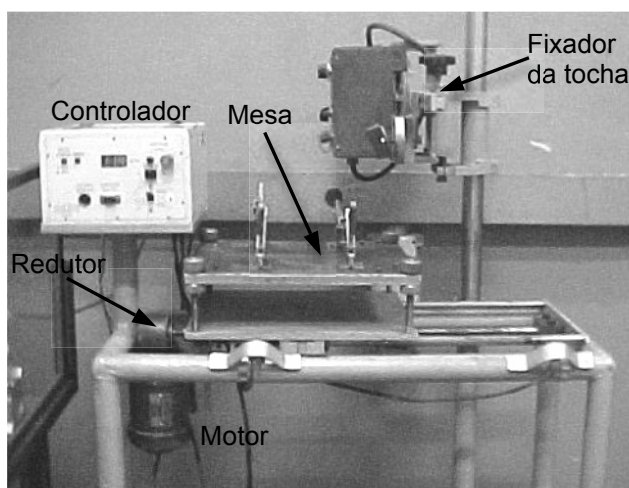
Sistema automático de soldagem com movimentação do corpo de prova.
